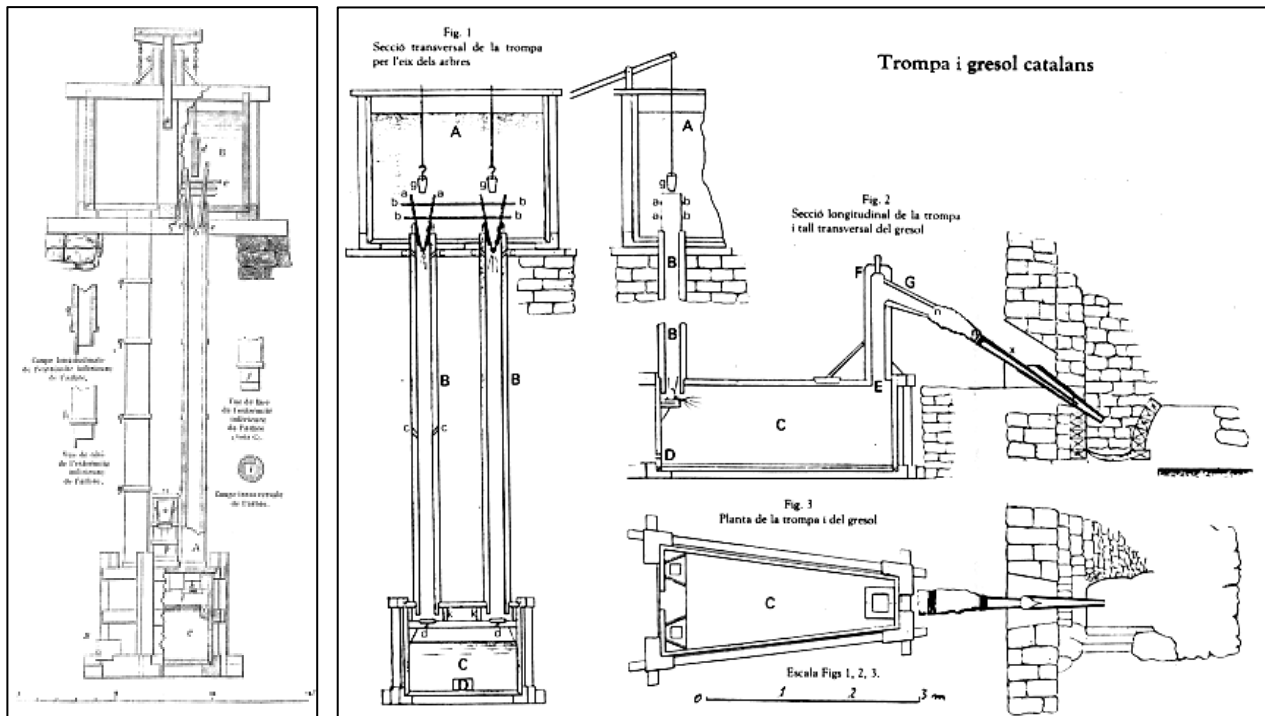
Planta, alzado y detalles de una trompa de agua. [2] y [3]
